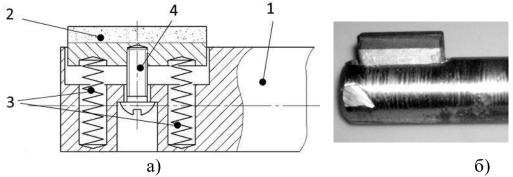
Головка для алмазної обробки отворів: а) схема будови; б) загальний вигляд
